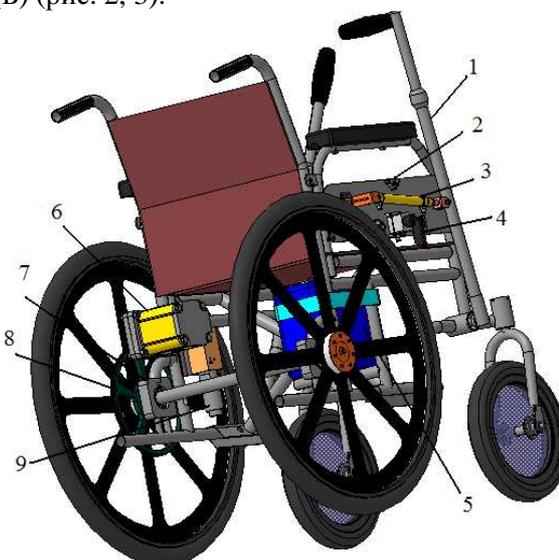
Компоновочная схема инвалидного кресла-коляски: 1 – рычаг управления; 2 – тройник; 3 – гидроцилиндр; 4 – гидрораспределитель; 5 – гидробак с фильтроэлементом; 6 – гидромотор; 7 – подшипник; 8 – редуктор; 9 – предохранительный клапан
